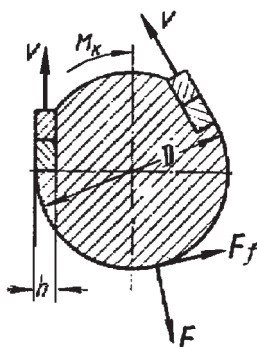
Нагрузки в шпоночном соединении с тангенциальными шпонками
